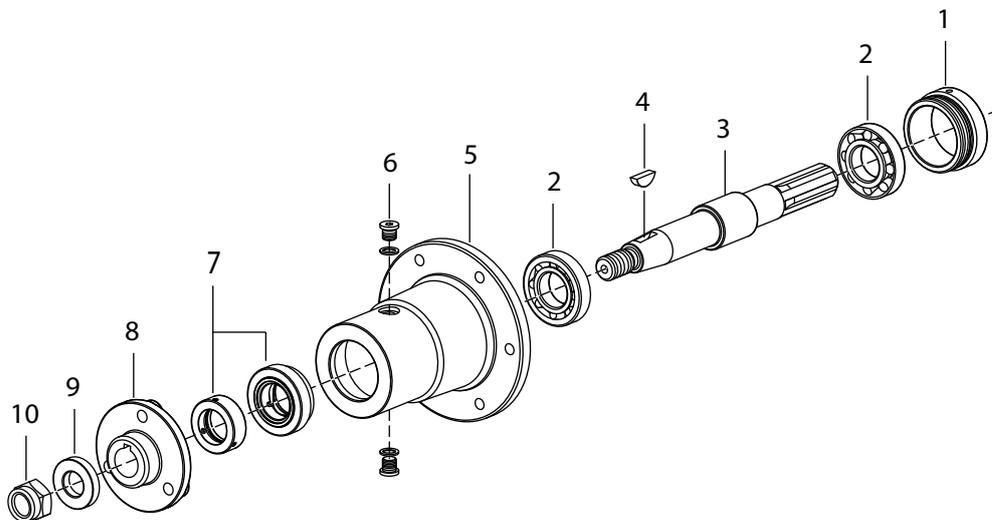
Aufbau Lagerflansch F7 mit Flügelaufnahme
